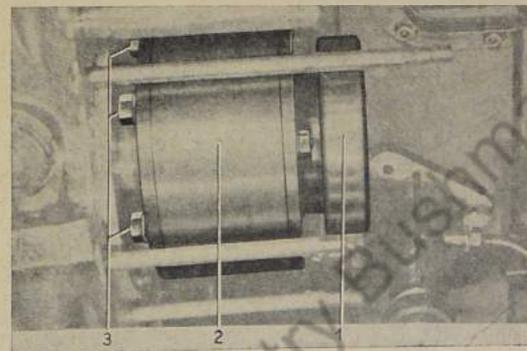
Freilaufsperr von Hauptwelle abschrauben
